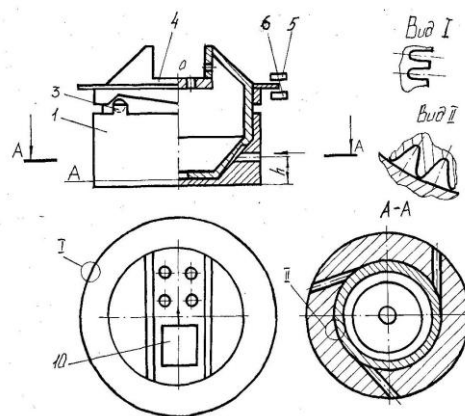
Устройство для бесконтактных взвешивания и сортировки штучных изделий по массе: 1 - корпус; 2 - дроссели для подачи сжатого воздуха; 3 - шаровая опора; 4 - промежуточная платформа - ротор; 5 - источник светового сигнала; 6 - фотозлемент; 7 - изделие.
